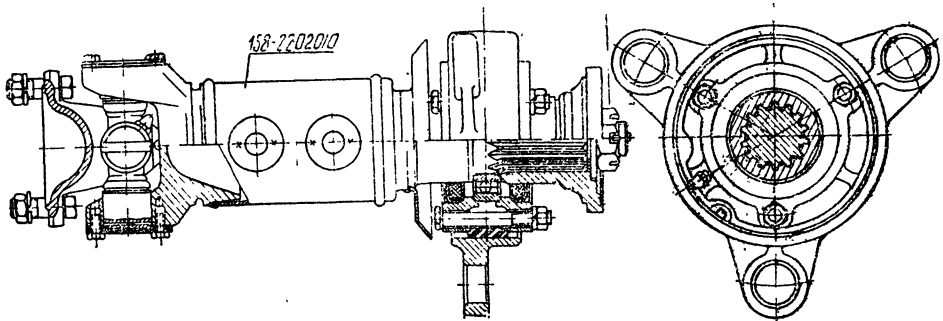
Промежуточный карданный вал с опорой автобуса ЗИЛ-158
